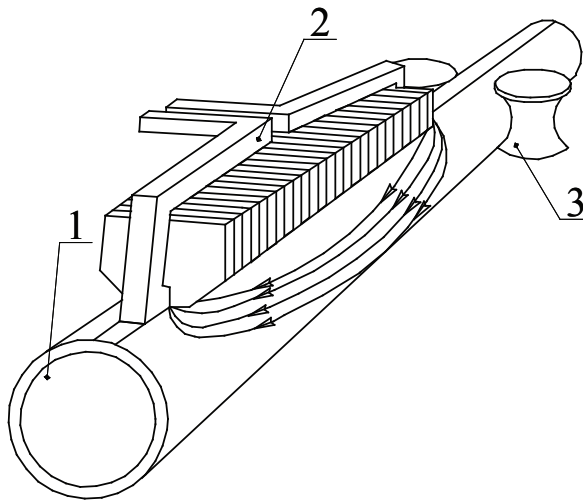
Принципиальная схема индукционной сварки труб:
